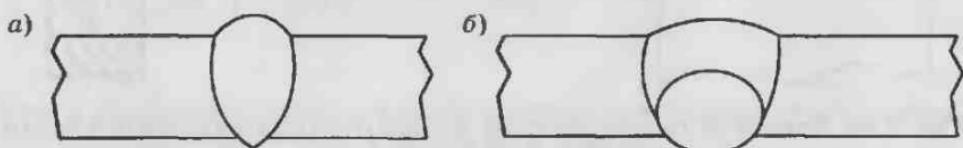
Виды сварных соединений по количеству наложения слоев: *а* — однослойное; *б* — многослойное
